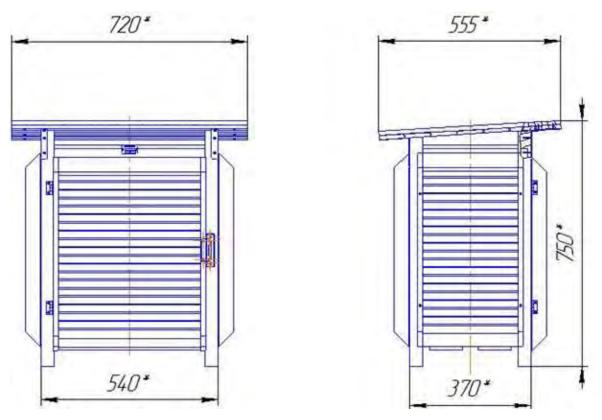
Габаритный чертеж будки психрометрической БП-1
